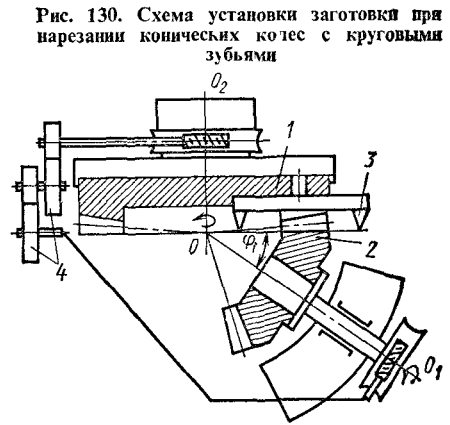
Схема установки заготовки при нарезании конических колес с круговыми зубьями
